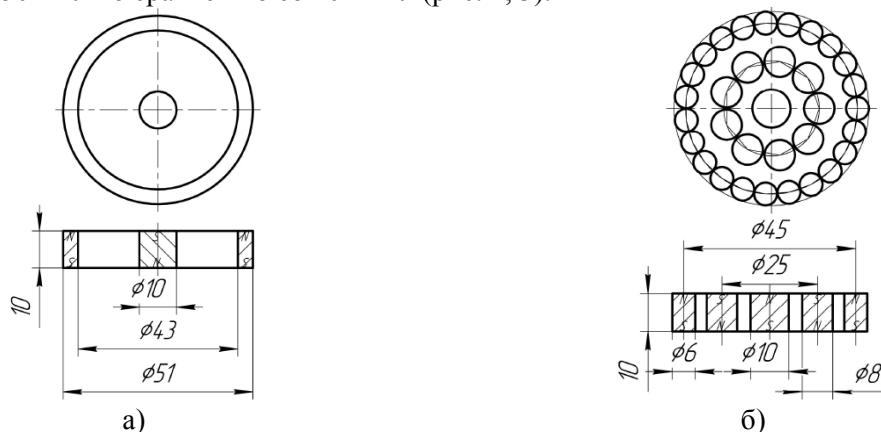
Конструкции магнитных систем магнетрона НМСА-52М: а) с цилиндрическими и кольцевым магнитами; б) с двумя областями плазмы.
